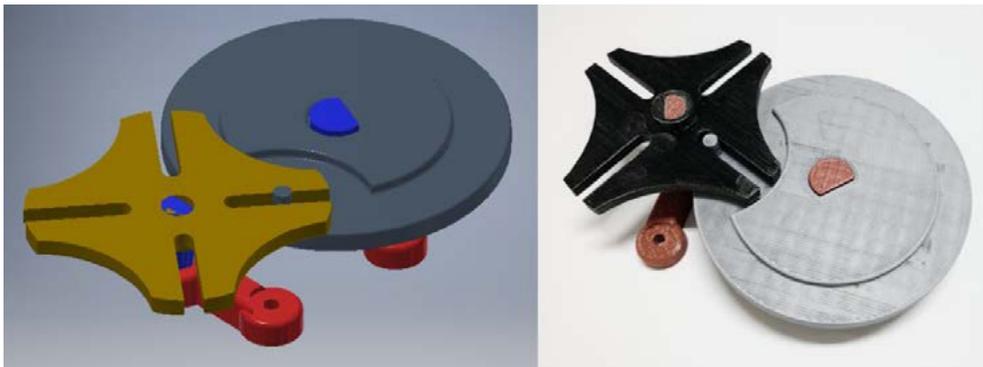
A la izquierda, conjunto ensamblado digitalmente y a la derecha, conjunto impreso en PLA. Imágenes de los autores.
